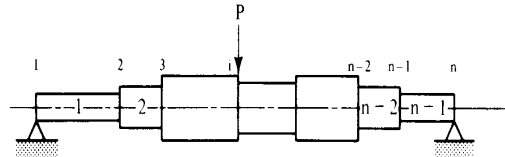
Viga simplemente apoyada de rigidez variable.
